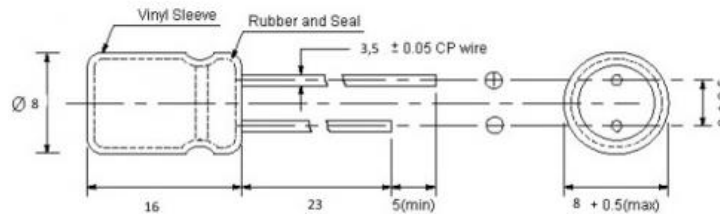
Габаритні розміри конденсатора типу b41828"Еrcos"
